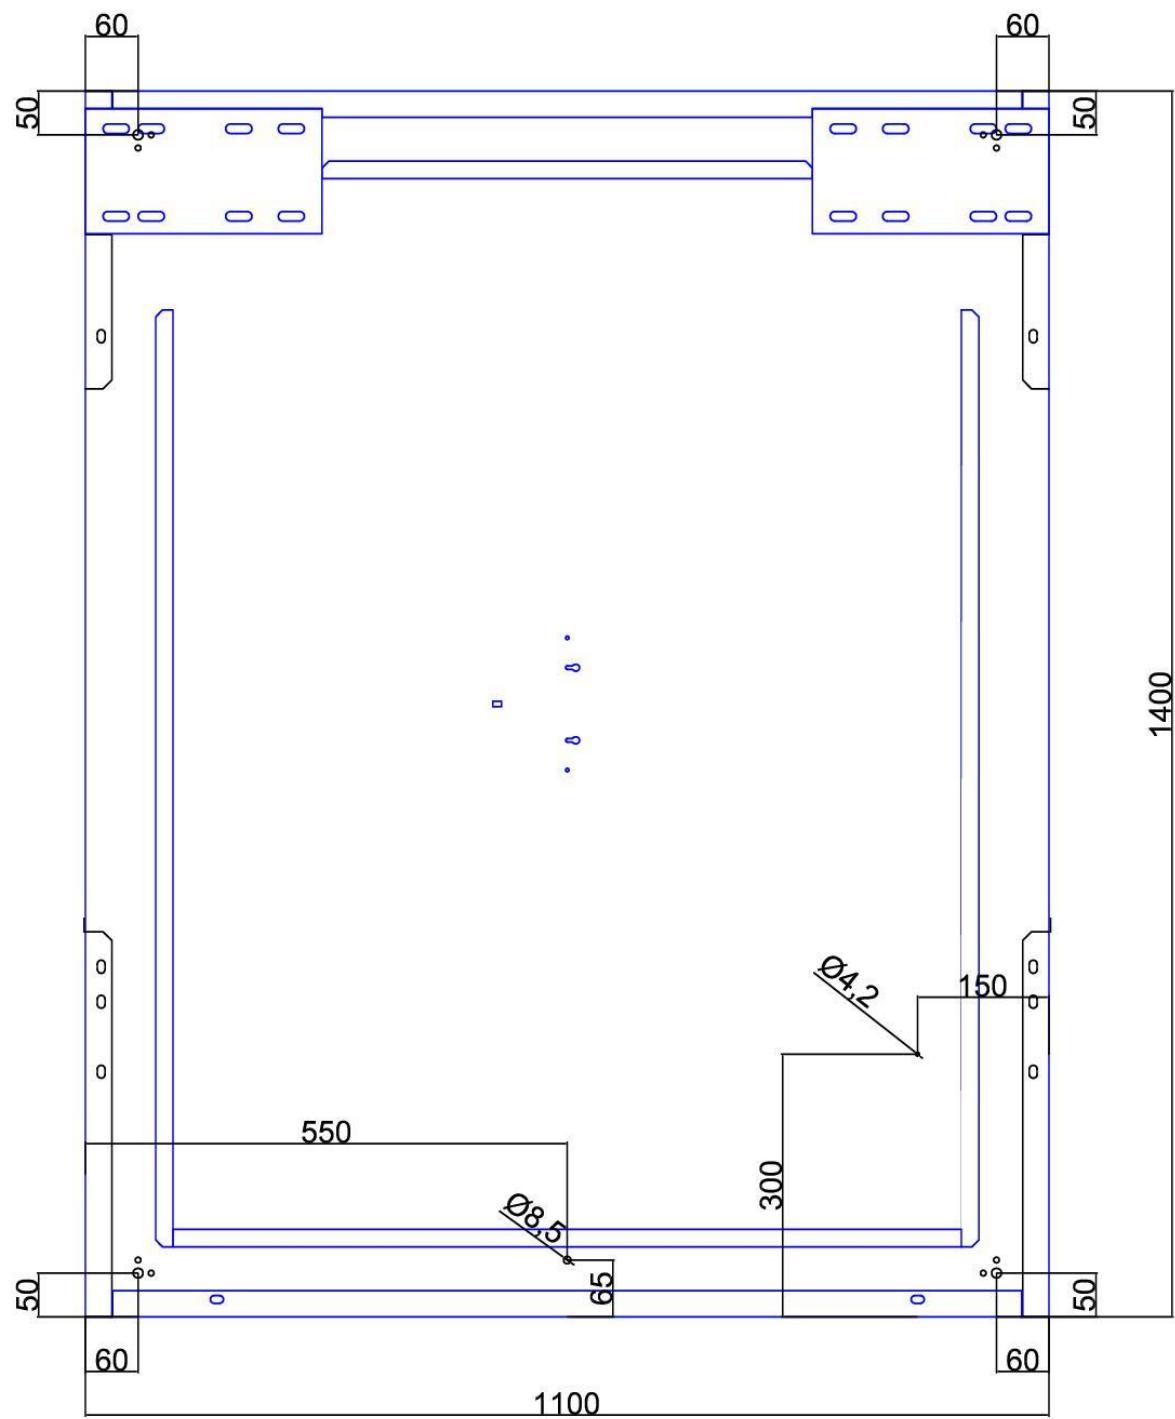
«Разметка и сверление отверстий под ввод кабеля и клемму заземления 630 кг»
